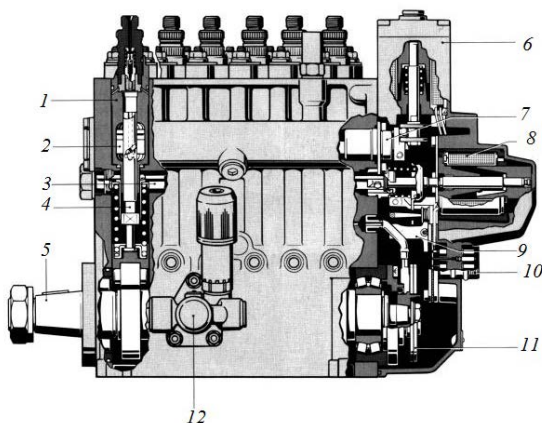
Рядный ТНВД с электронным управлением: 1 – гильза; 2 – втулка управления; 3 – рейка подачи топлива; 4 – плунжер; 5 – кулачковый вал; 6 – электромагнитный клапан начала подачи топлива; 7 – вал управления регулирующей втулкой; 8 – электромагнитный регулятор количества топлива; 9 – индуктивный датчик положения рейки; 10 – вилочное соединение; 11 – диск; 12 – топливopодкачивающий насос
